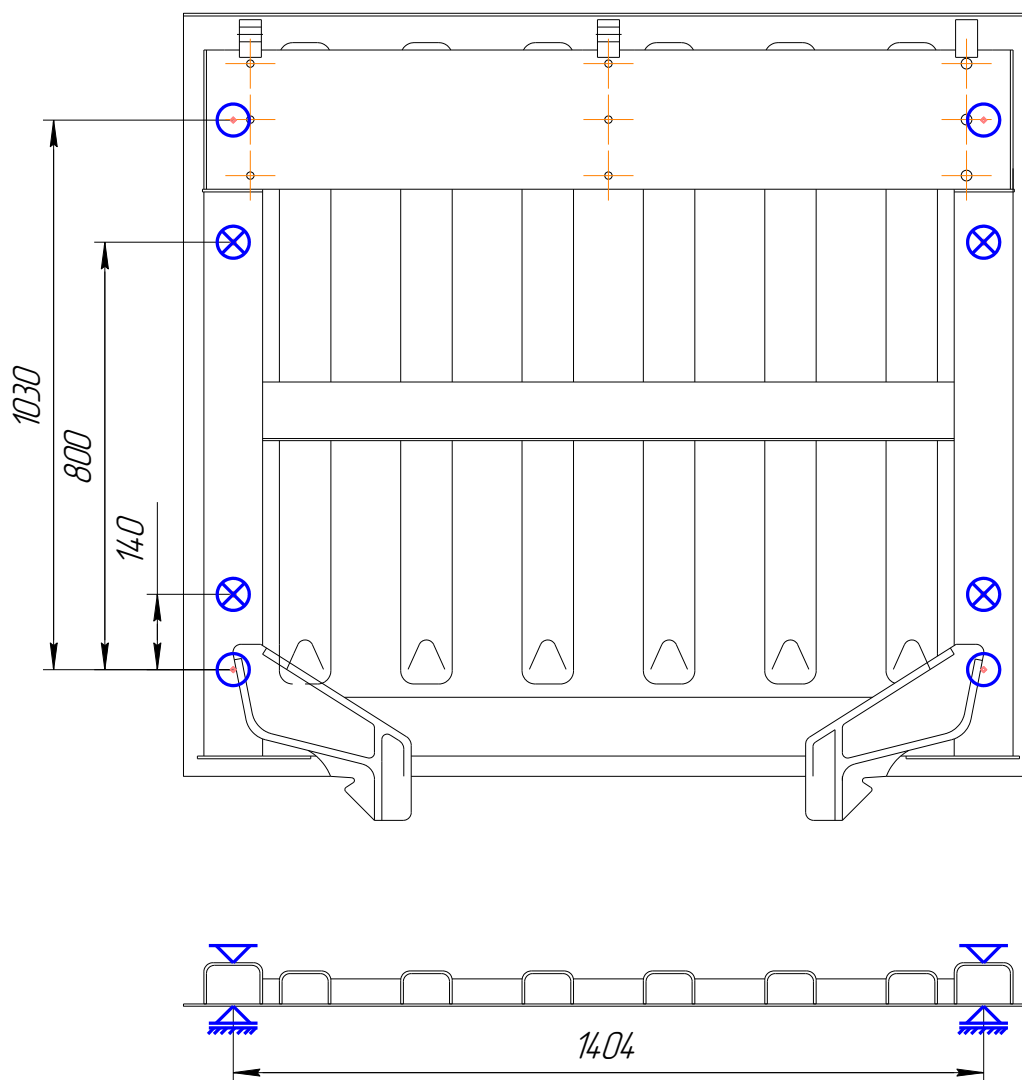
Принципиальная схема сборочно-сварочного приспособления
